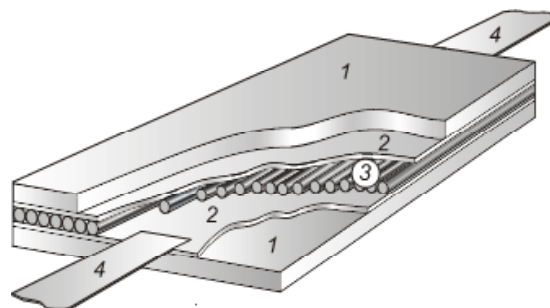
Схема сборки пакета из заготовок листовых матричных сплавов и армирующей сетки для сварки композиционного материала:
